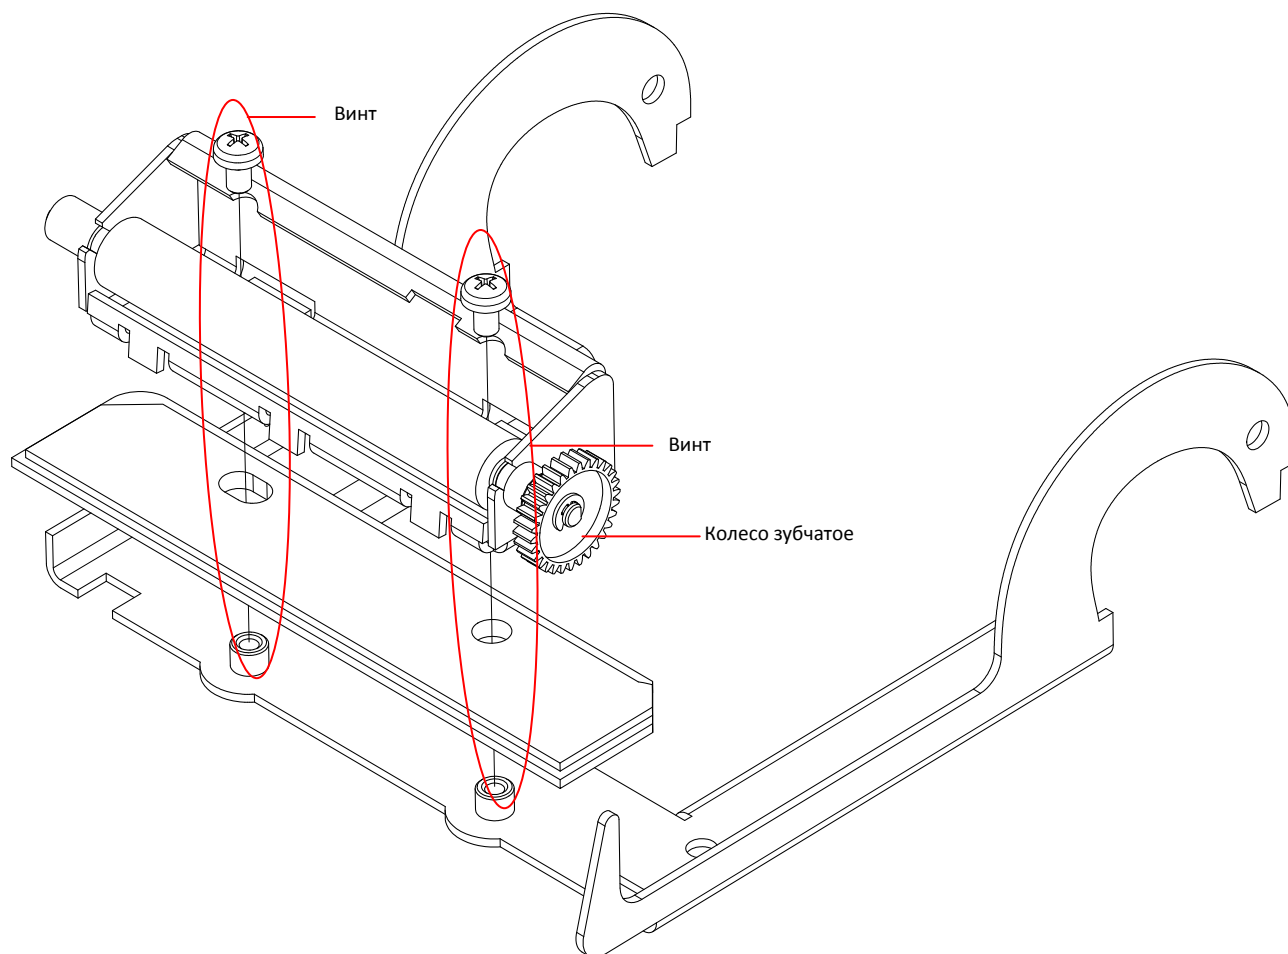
Крепление ножа отрезчика и механизма прижимного вала чековой ленты.
